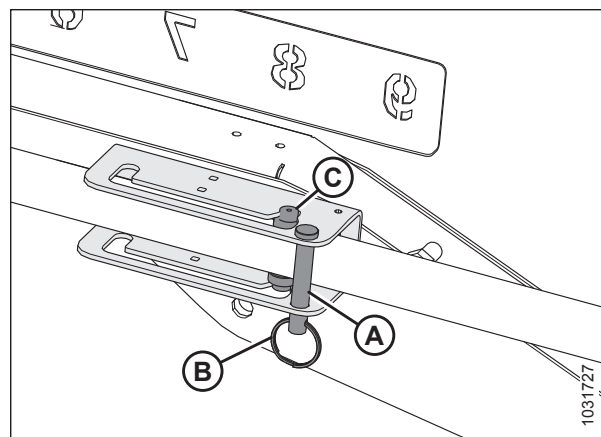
Cilindrul brațului stâng – poziția spre spate
